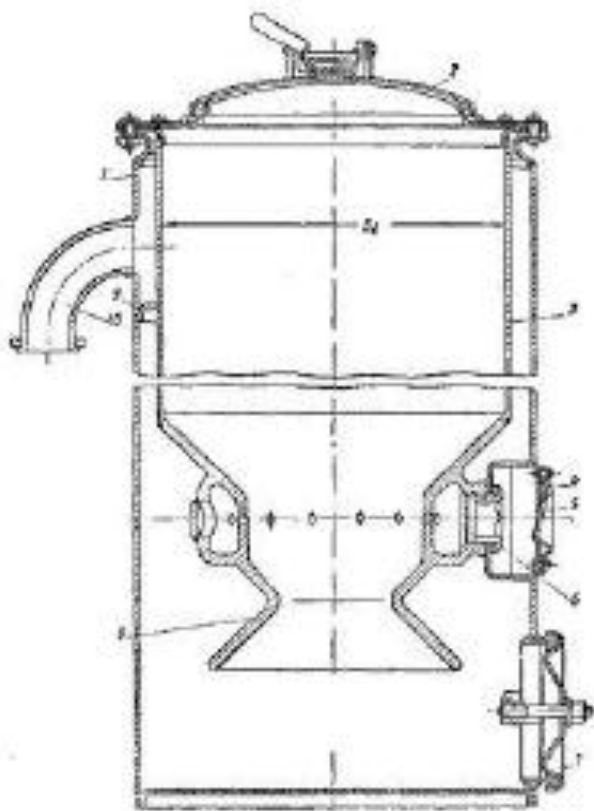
Газогенератор ГАЗ-42: 1-корпус; 2-завантажувальна кришка; 3-паливний бункер; 4-клапанна коробка; 5-зворотний клапан; 6- футорка; 7-золотниковий люк; 8-спідниця камери газифікації; 9-відбивач; 10-газовідбірний патрубок.
